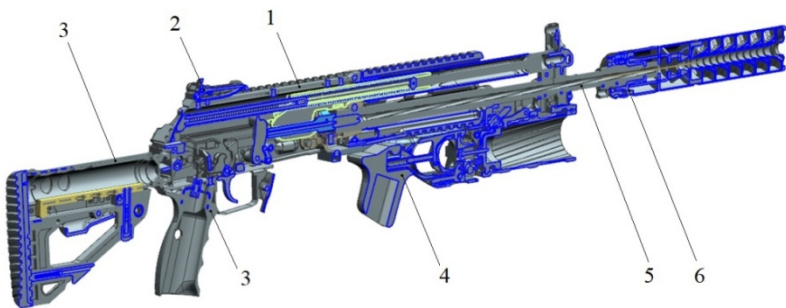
Автоматическое стрелковое оружие с внешними навесными устройствами: 1 – ствольная коробка; 2 – прицельное приспособление диоптрического типа; 3 – приклад и рукоятка пистолетного типа; 4 – подствольный гранатомет; 5 – ствол; 6 – прибор малошумной стрельбы)
